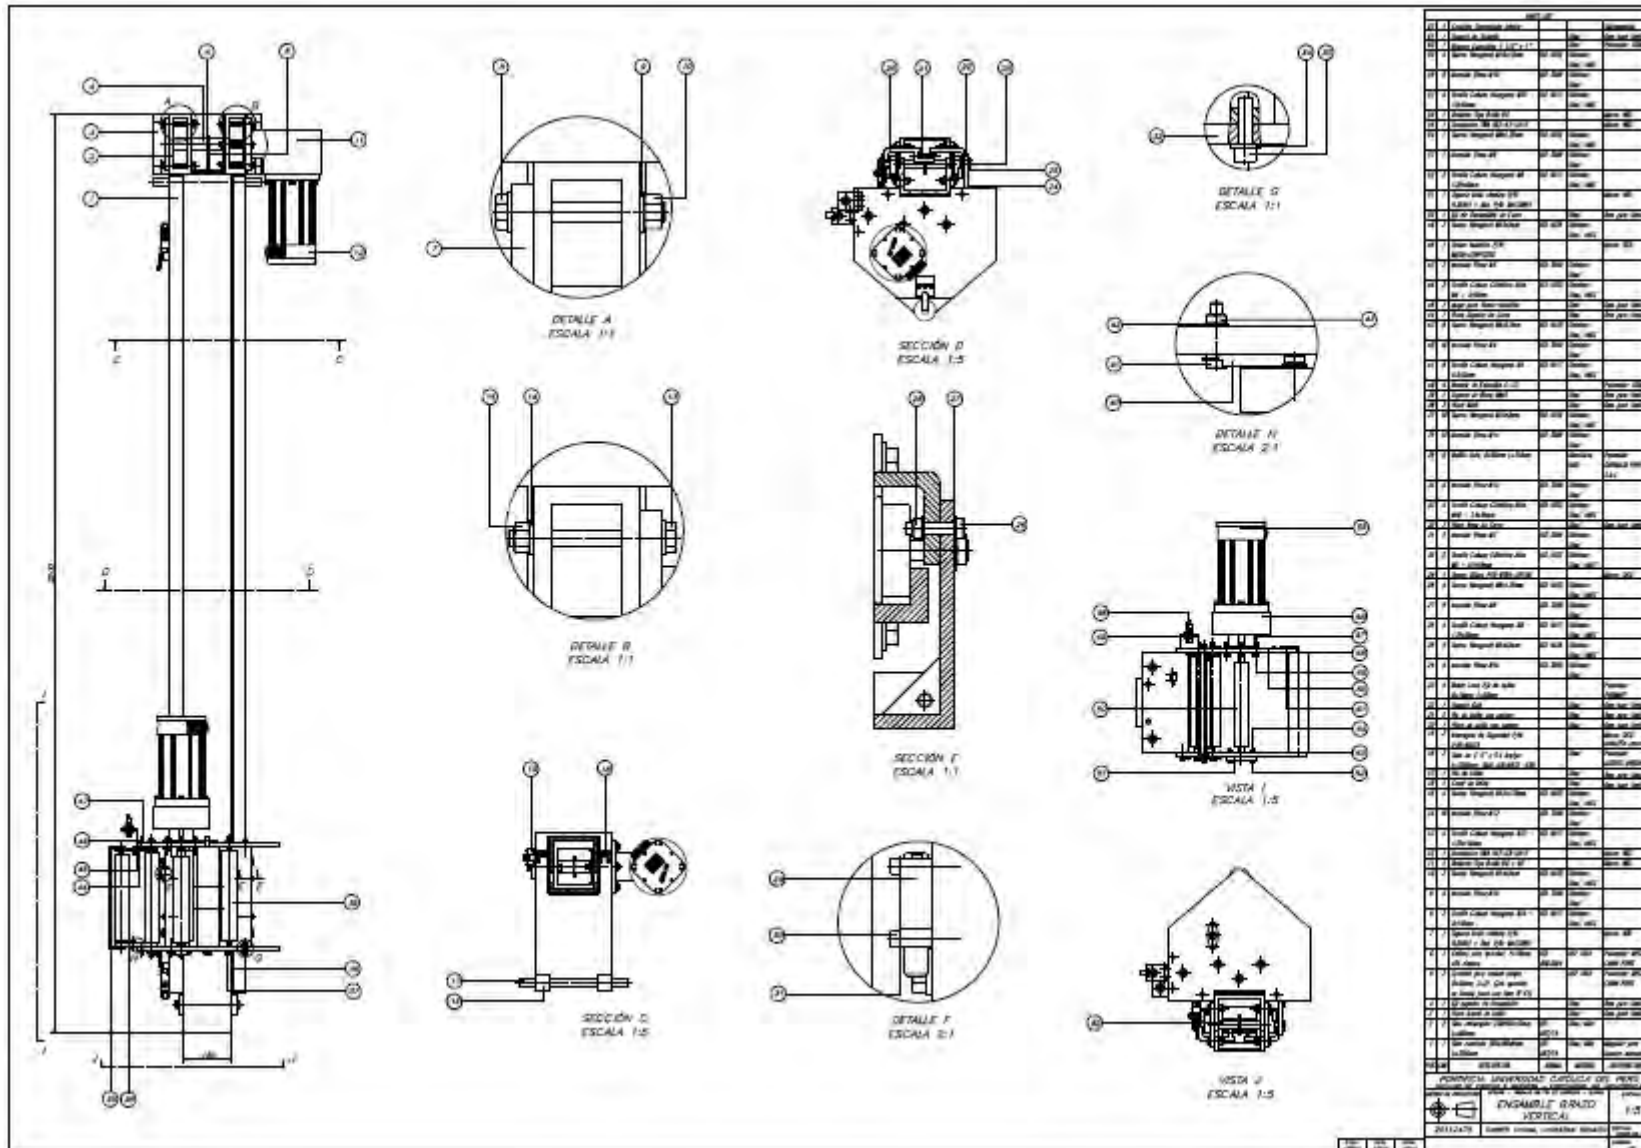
Parte vertical de brazo giratorio. Plano. Fuente: Propia.
